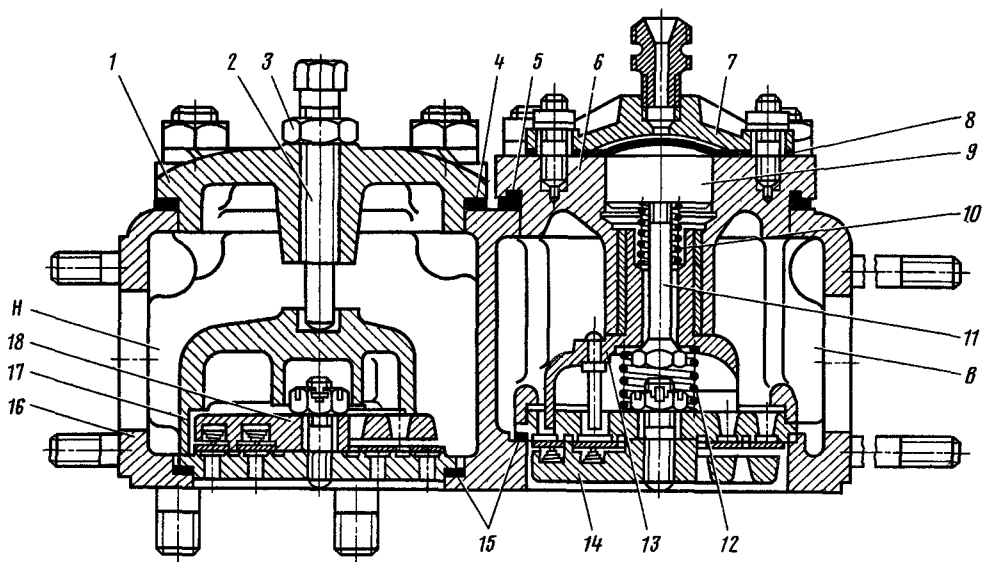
Клапанная коробка цилиндра первой ступени сжатия
